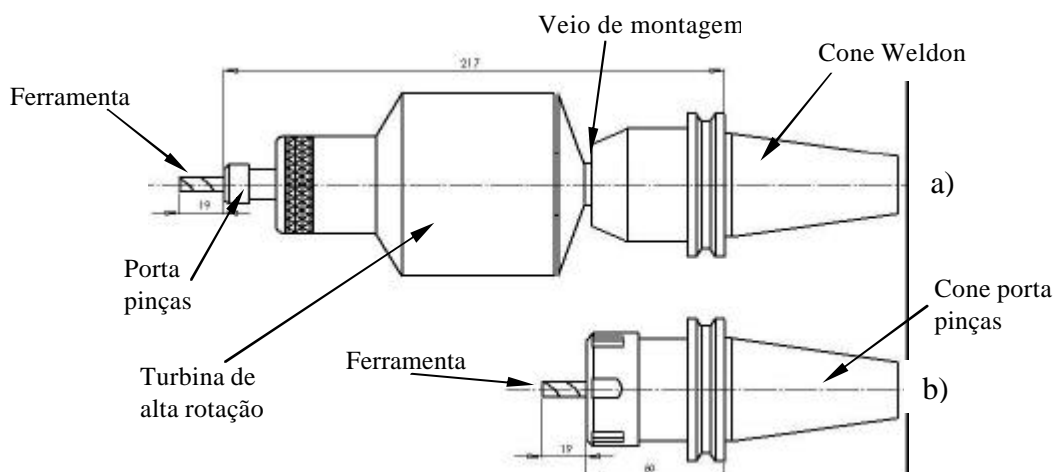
Montagem da ferramenta na turbina de alta rotação (a) e montagem standard (b)
